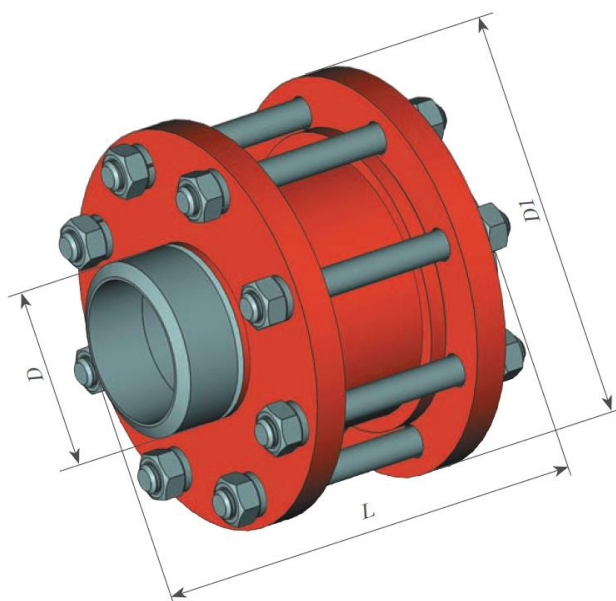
Общий вид клапана обратного магистрального для Ду80, Ду100, Ду150
